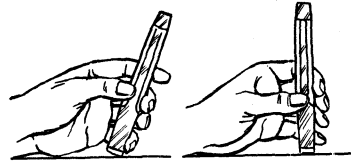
Установка зубила при рубке листового металла на наковальне или плите
